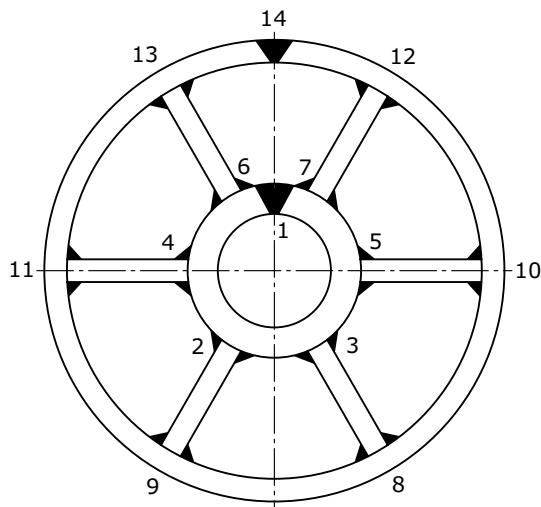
ueZ) Schweißfolgeplan eines Treibrades
